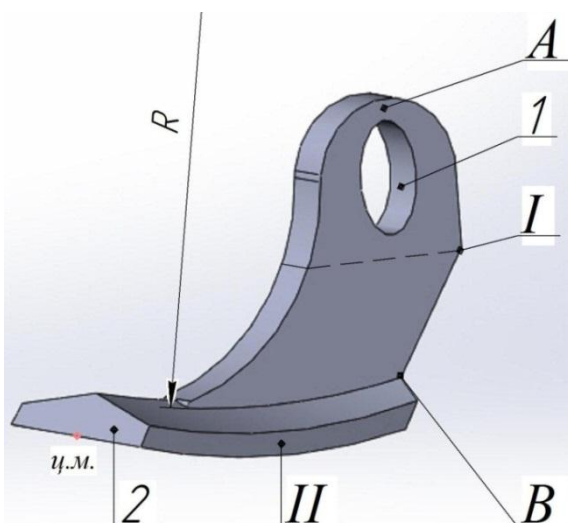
Предлагаемая конструкция ножа ротационной косилки-измельчителя
